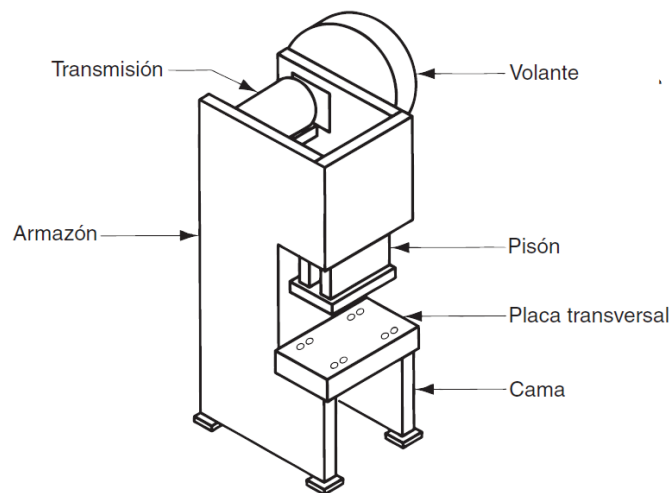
Componentes de prensa troqueladora típica mecánica.
